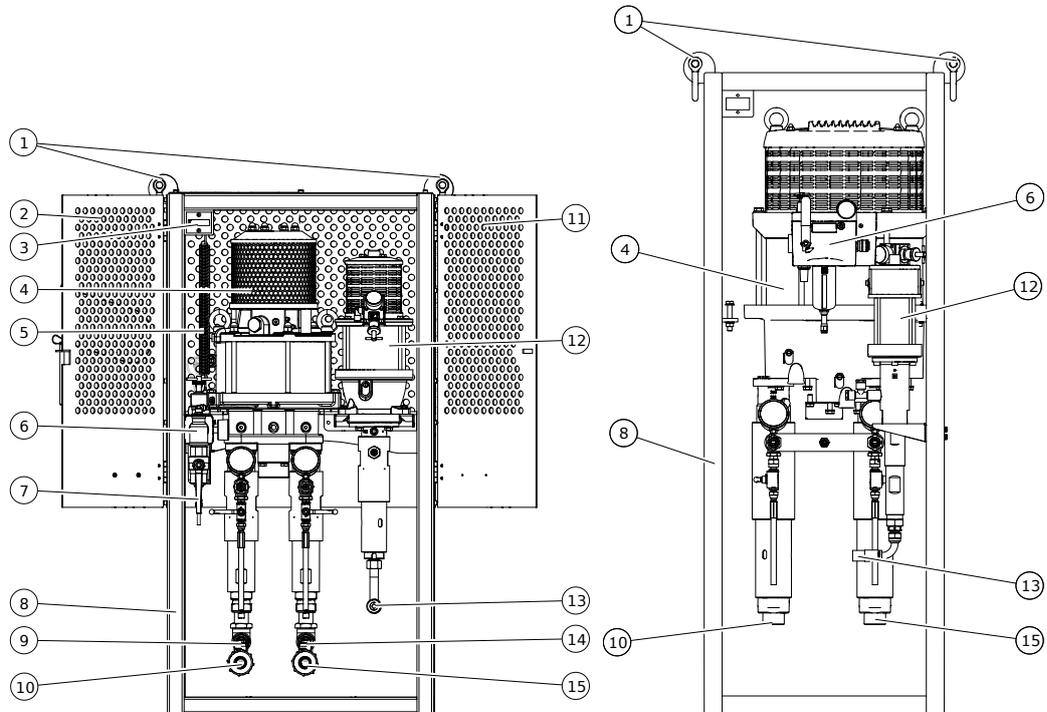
Aufbau Inject 230 ohne Steuerschrank
